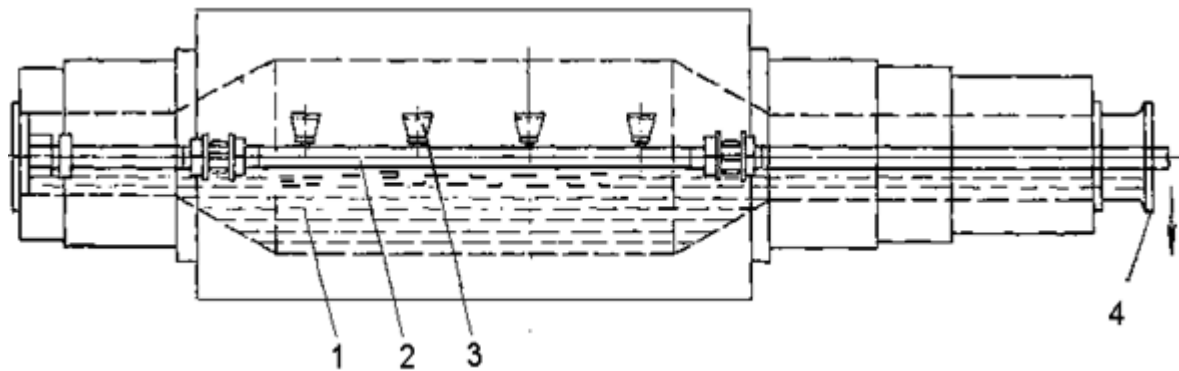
Схема охолодження валків: 1 — валок; 2 — труба охолодження; 3 — розбризкуючи пристрої; 4 — зливна воронка
